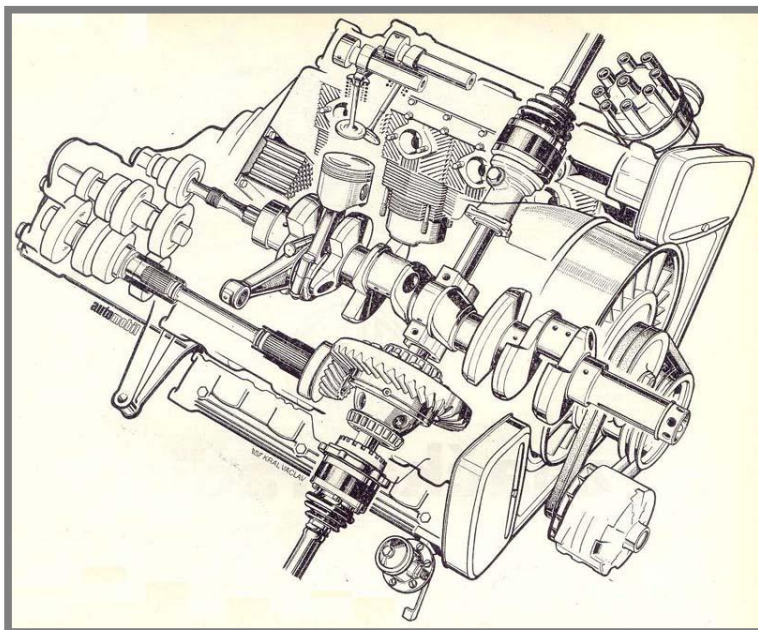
Motor uložený za zadní nápravou - Porsche 911 Turbo [24]
